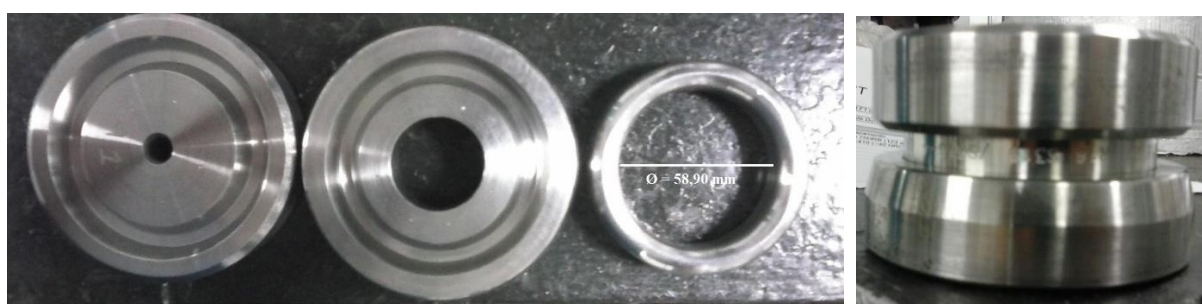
Parte superior e inferior do flange e anel (esquerda); conjunto montado (direita).
